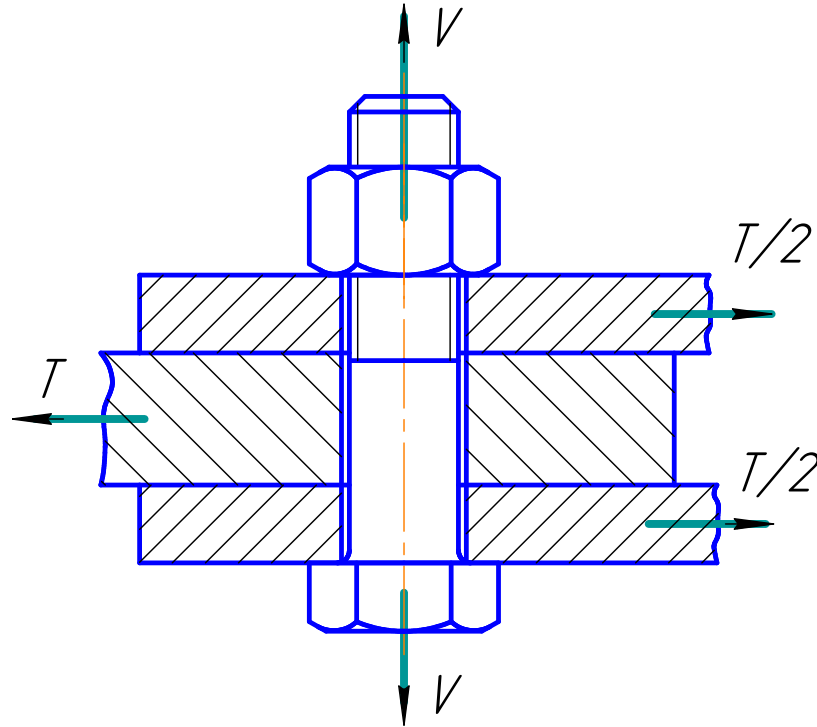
Схема для розрахунку болтового з'єднання, навантаженого поперечною силою
